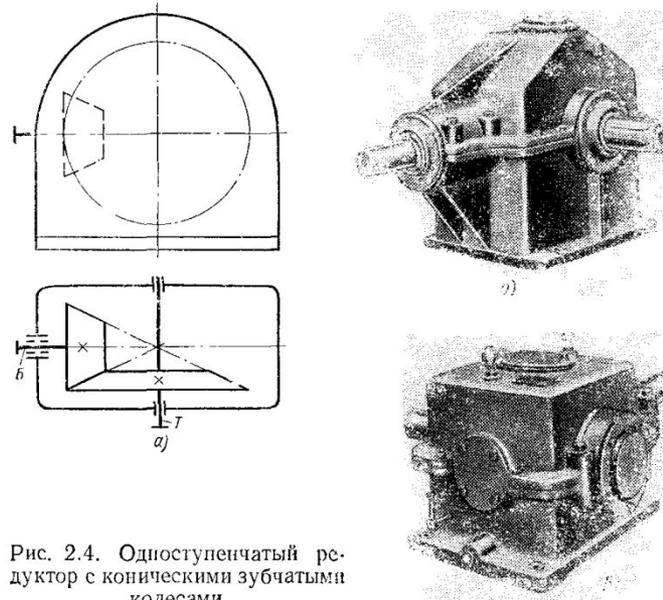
Одноступенчатый редуктор с коническими зубчатыми колесами
